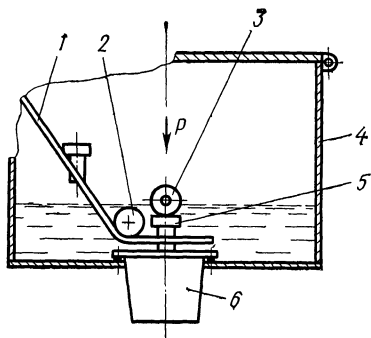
Схема очистки деталей контактным способом — прижимом детали к излучателю:
